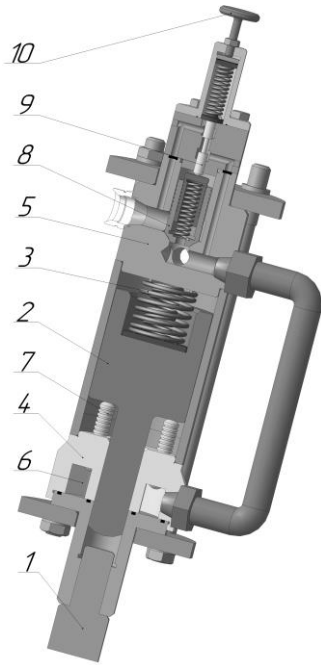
Конструктивна схема віброударного пристрою для руйнування гірських порід
